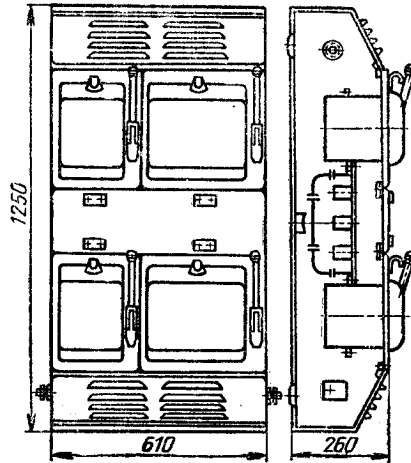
Габаритные размеры распределительных пунктов ПРБ-59-41 и ПРБ-59-43.
